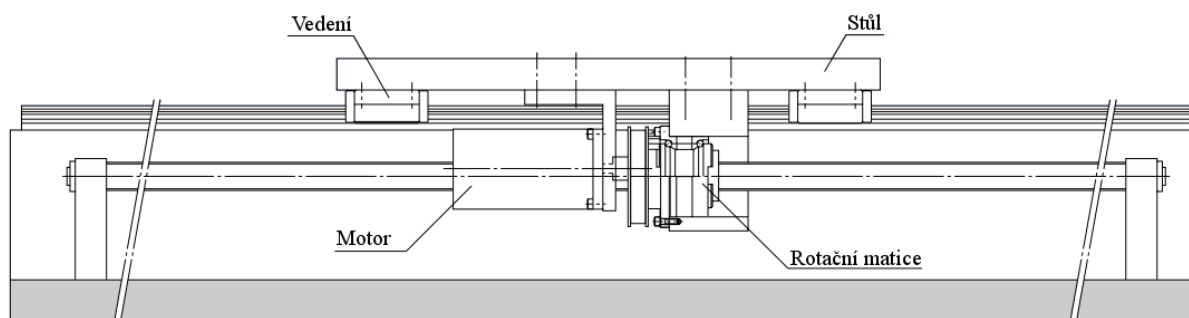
Řez motorem s dutým rotorem a upevněným KŠM [STÖBER] [23]
